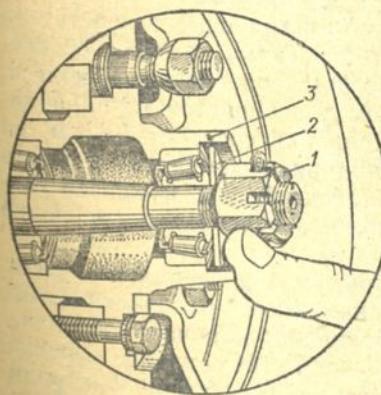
Проверка затяжки подшипников ступицы переднего колеса:
